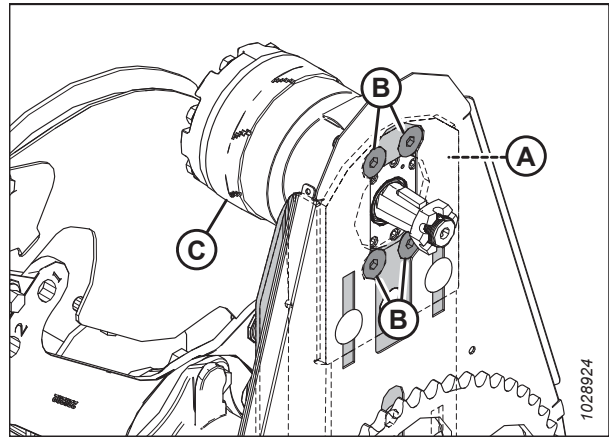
Befestigungsschrauben am Haspelantriebsmotor
